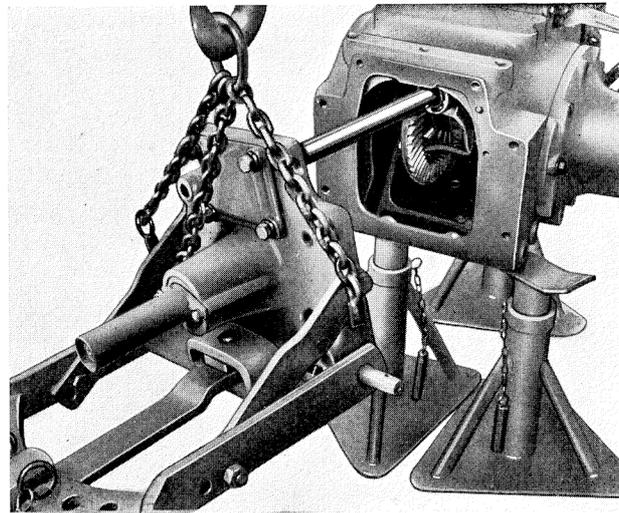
Dépose du couvercle arrière du carter de transmission finale.
